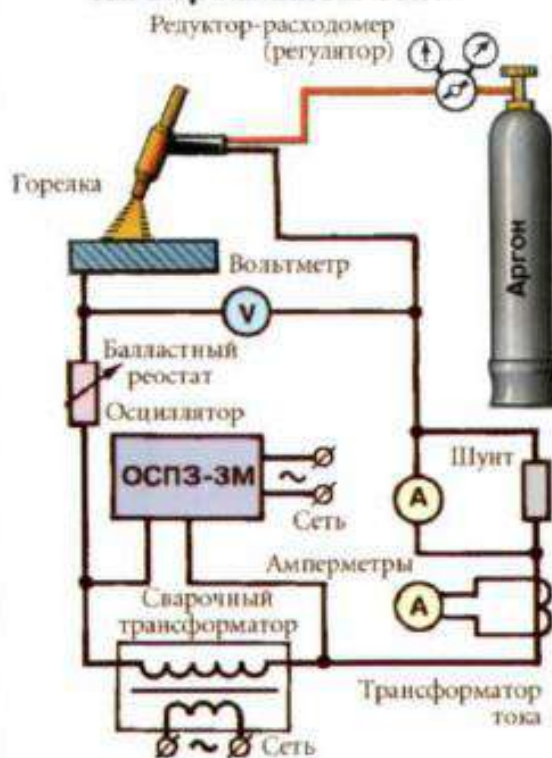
Схема оборудования для сварки на переменном токе.
